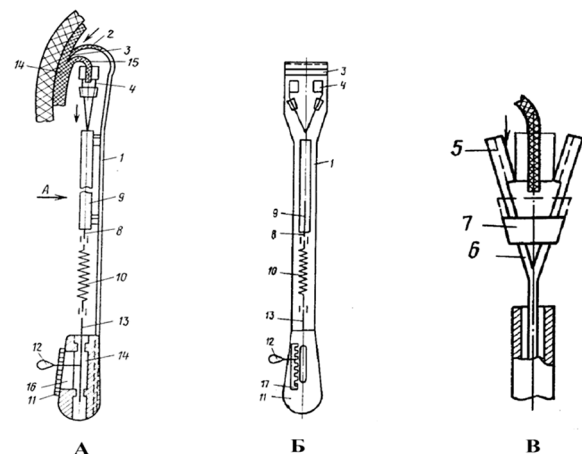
Внешний вид хирургического инструмента, состоящего из: 1 – рукоятка; 2 – крючкообразное лезвие; 3 – режущая кромка; 4 – два зажима с губками; 5,6 – бранши; 7 – скользящие фиксаторы; 8 – натяжной механизм; 9 – трубка для тяги; 10 – пружина; 11 – зубчатая рейка; 12 – рычаг; 13 – тяга для зубчатой рейки; 14 – надрез твердой мозговой оболочки; 15 – дуальный листок; 16 – паз для рычага; 17 – ножи рукоятки.
